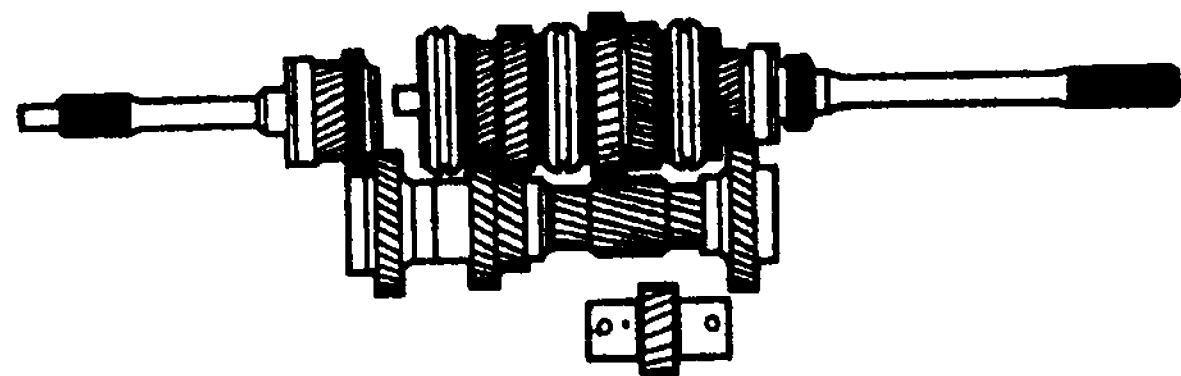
Валы и шестерни коробки передач после их сборки
